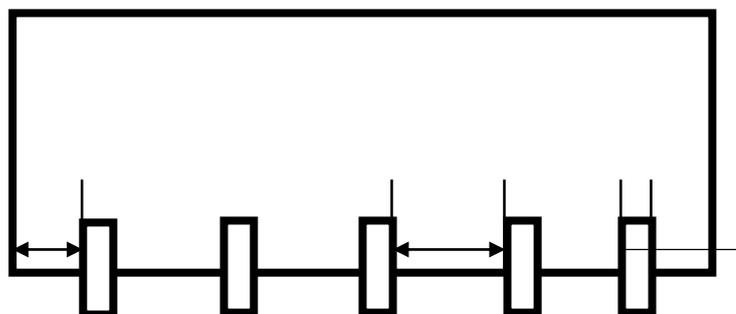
Схема расположения дополнительных зубьев по длине отвала бульдозера
